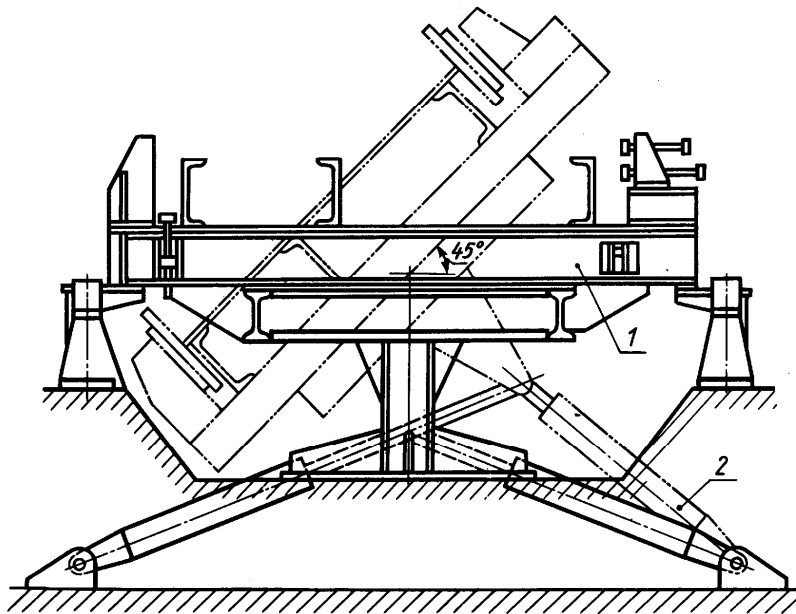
Схема полуповоротного специализированного кондуктора для сборки двутавровых балок
